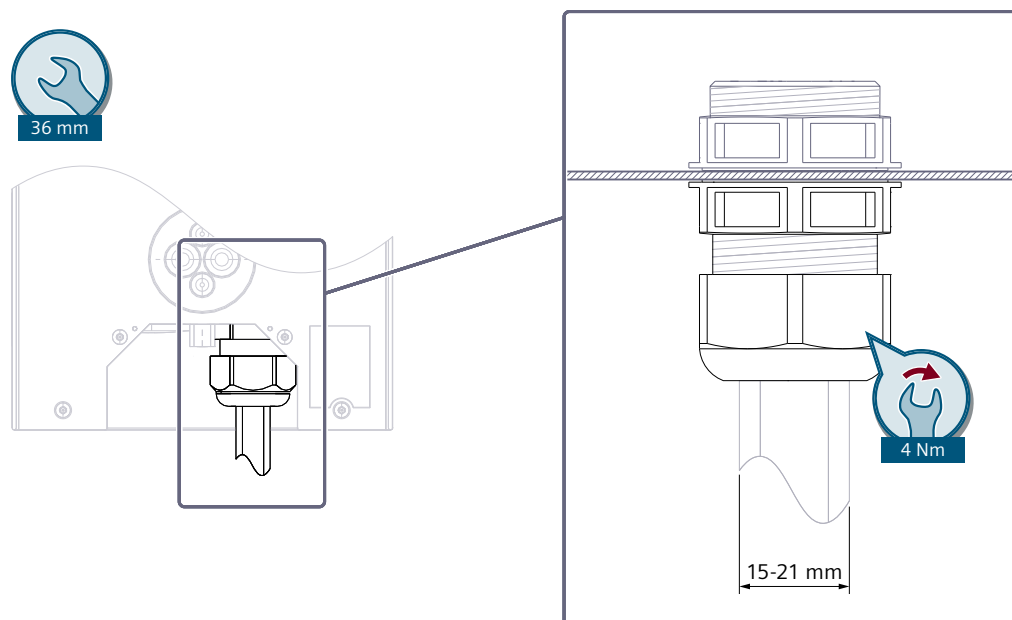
Alimentazione Wallbox 8EM1310-..0.-....
